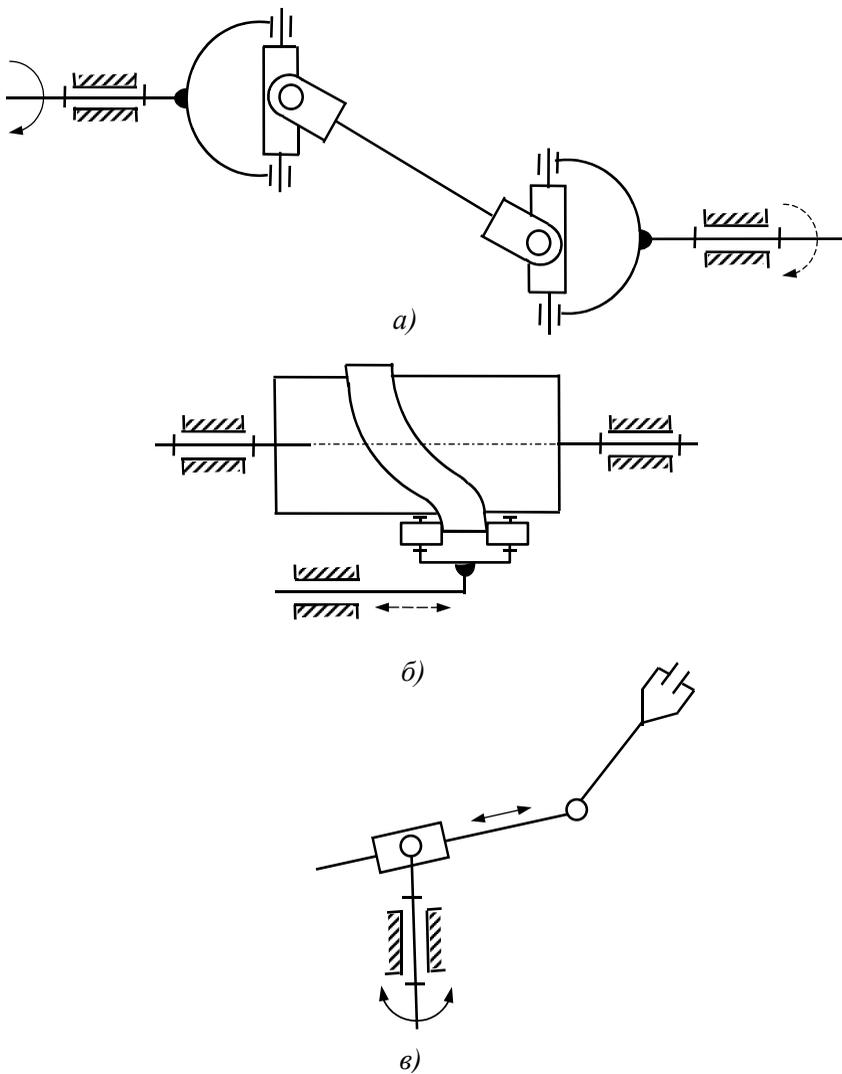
Схемы пространственных механизмов: а) механизма двойного универсального шарнира (карданова шарнира); б) кулачкового механизма; в) манипулятора
